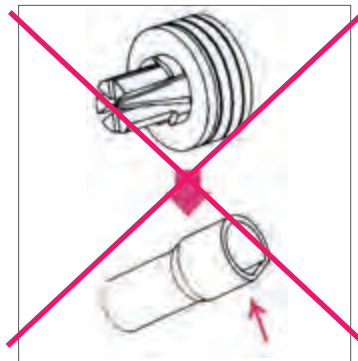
Повреждение трубы из-за дефектной расширительной насадки
